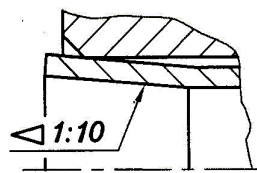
Конічне розвальцювання труби перед зварюванням
